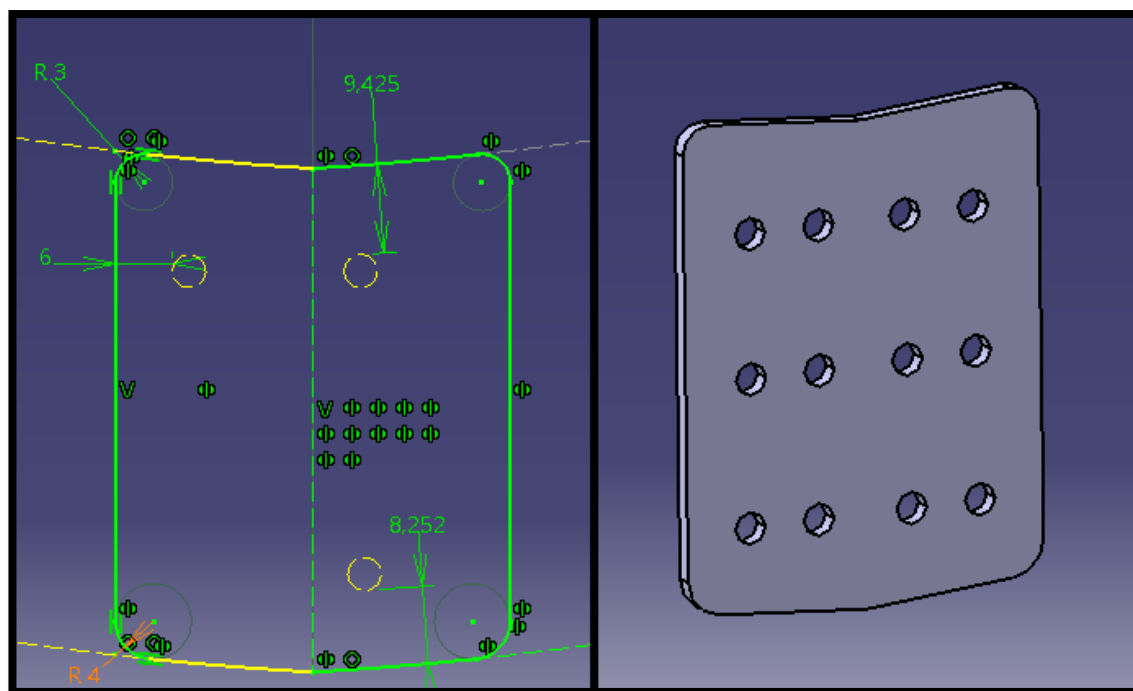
Refuerzo inferior 14: Sketch y pieza final tras extrusión y vaciado
